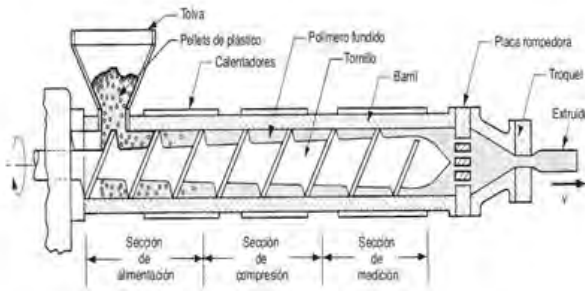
Esquema de extrusión de pellet por medio de tornillo sin fin.
